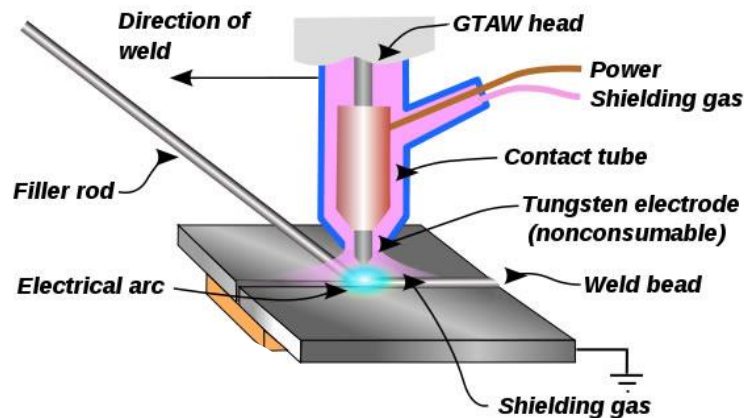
Esquema de soldadura tipo TIG
